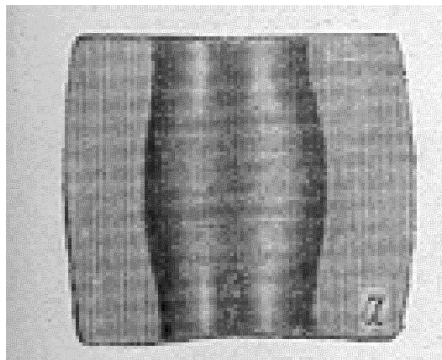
а – Формозміна тонкостінної кільцевої заготовки
